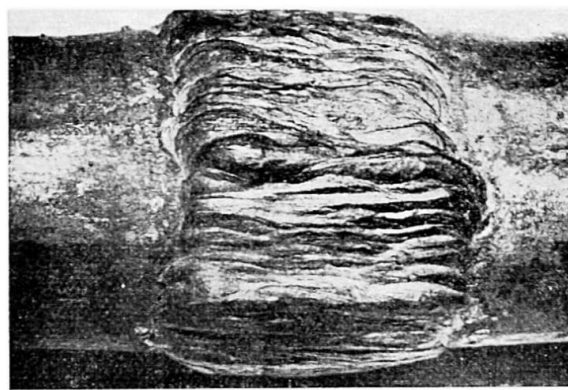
Aspect d'un joint soudé par soudure à l'arc d'une barre de 50 mm de diamètre.
